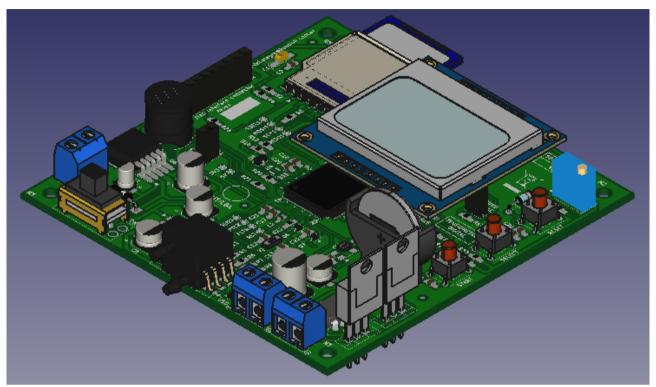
Vista 3D del PCB, vista axonométrica. (Con Display montado).
